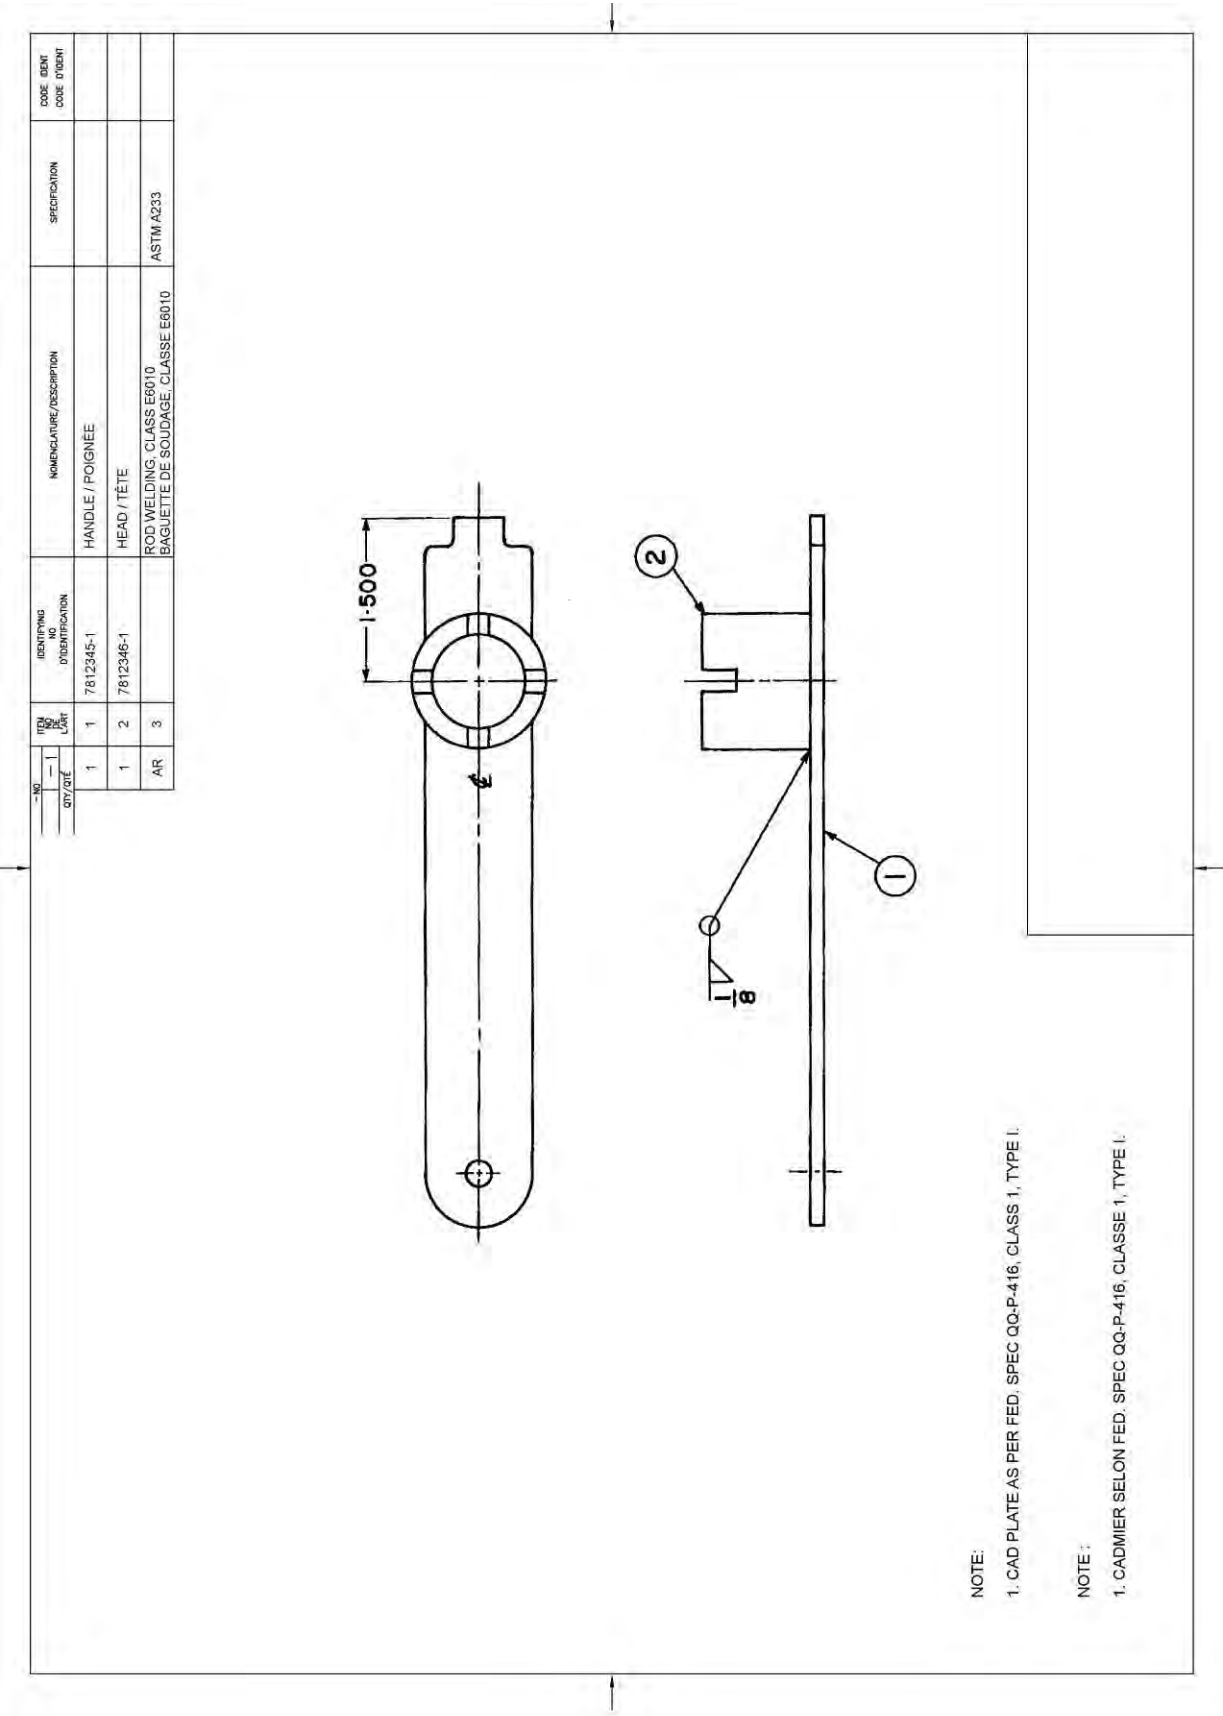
(feuille 1 de 2) Dessin d'ensemble inséparable
